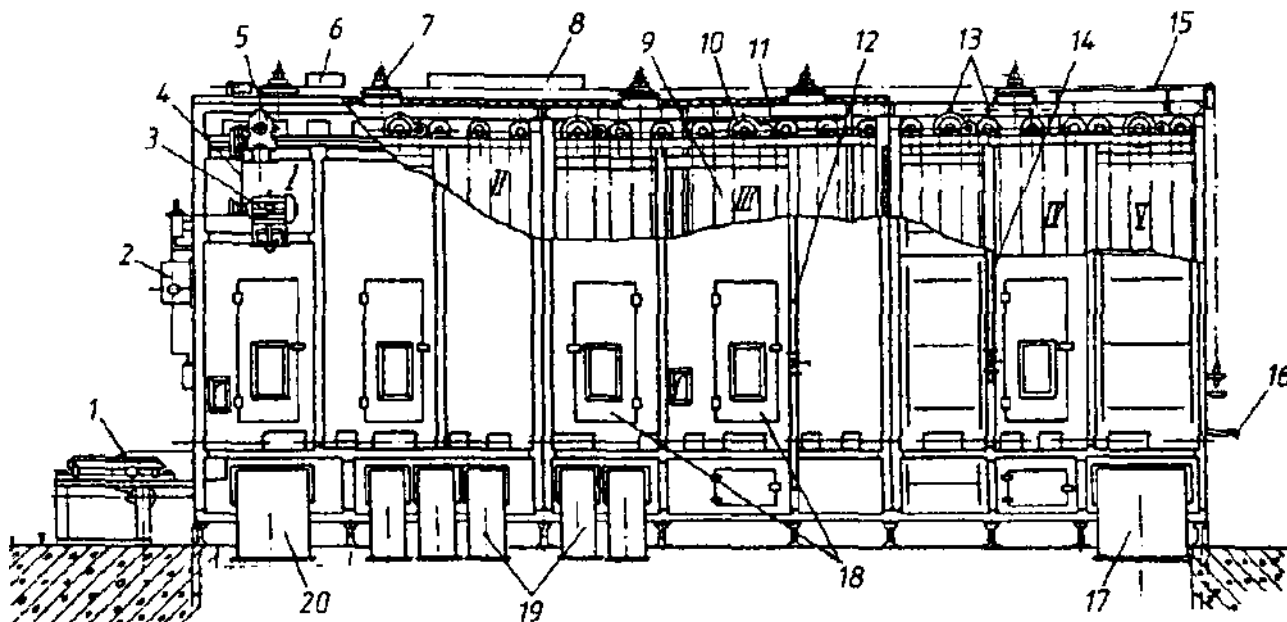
Ланцюговий термоагрегат для теплової обробки сосисок: 1 – вузол завантаження; 2 – привід струшувача, 3 – електродвигун, 4 – клинопасова передача; 5 – черв'ячний редуктор; 6, 8, 15 – димари для подачі гарячого повітря; 7 – ліхтар; 9 – ланцюг; 10 – зірочка; 11 – форсунки для пари; 12 – паропровід; 13 – перфоровані труби; 14 – трубопровід для холодної води; 16 – вузол розвантаження; 17, 19, 20 – патрубки для відводу відпрацьованих газів; 18 – двері
